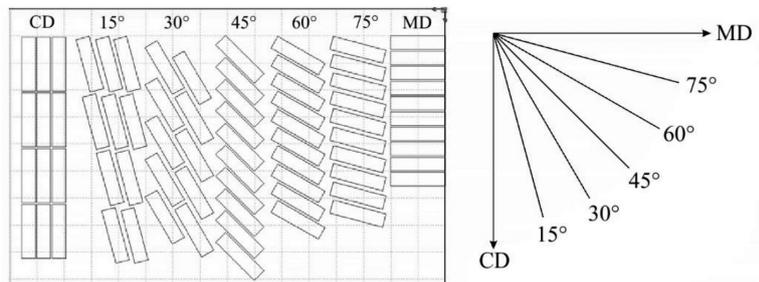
Рабочий эскиз для лазерной резки элементов изделий с различным углом расположения линий склейки гофров
